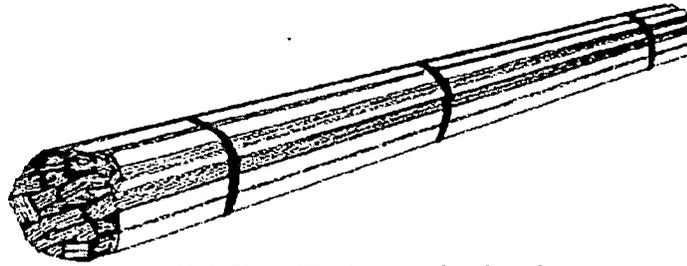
Lift de Planos (Flats) Asegurado Adecuadamente
